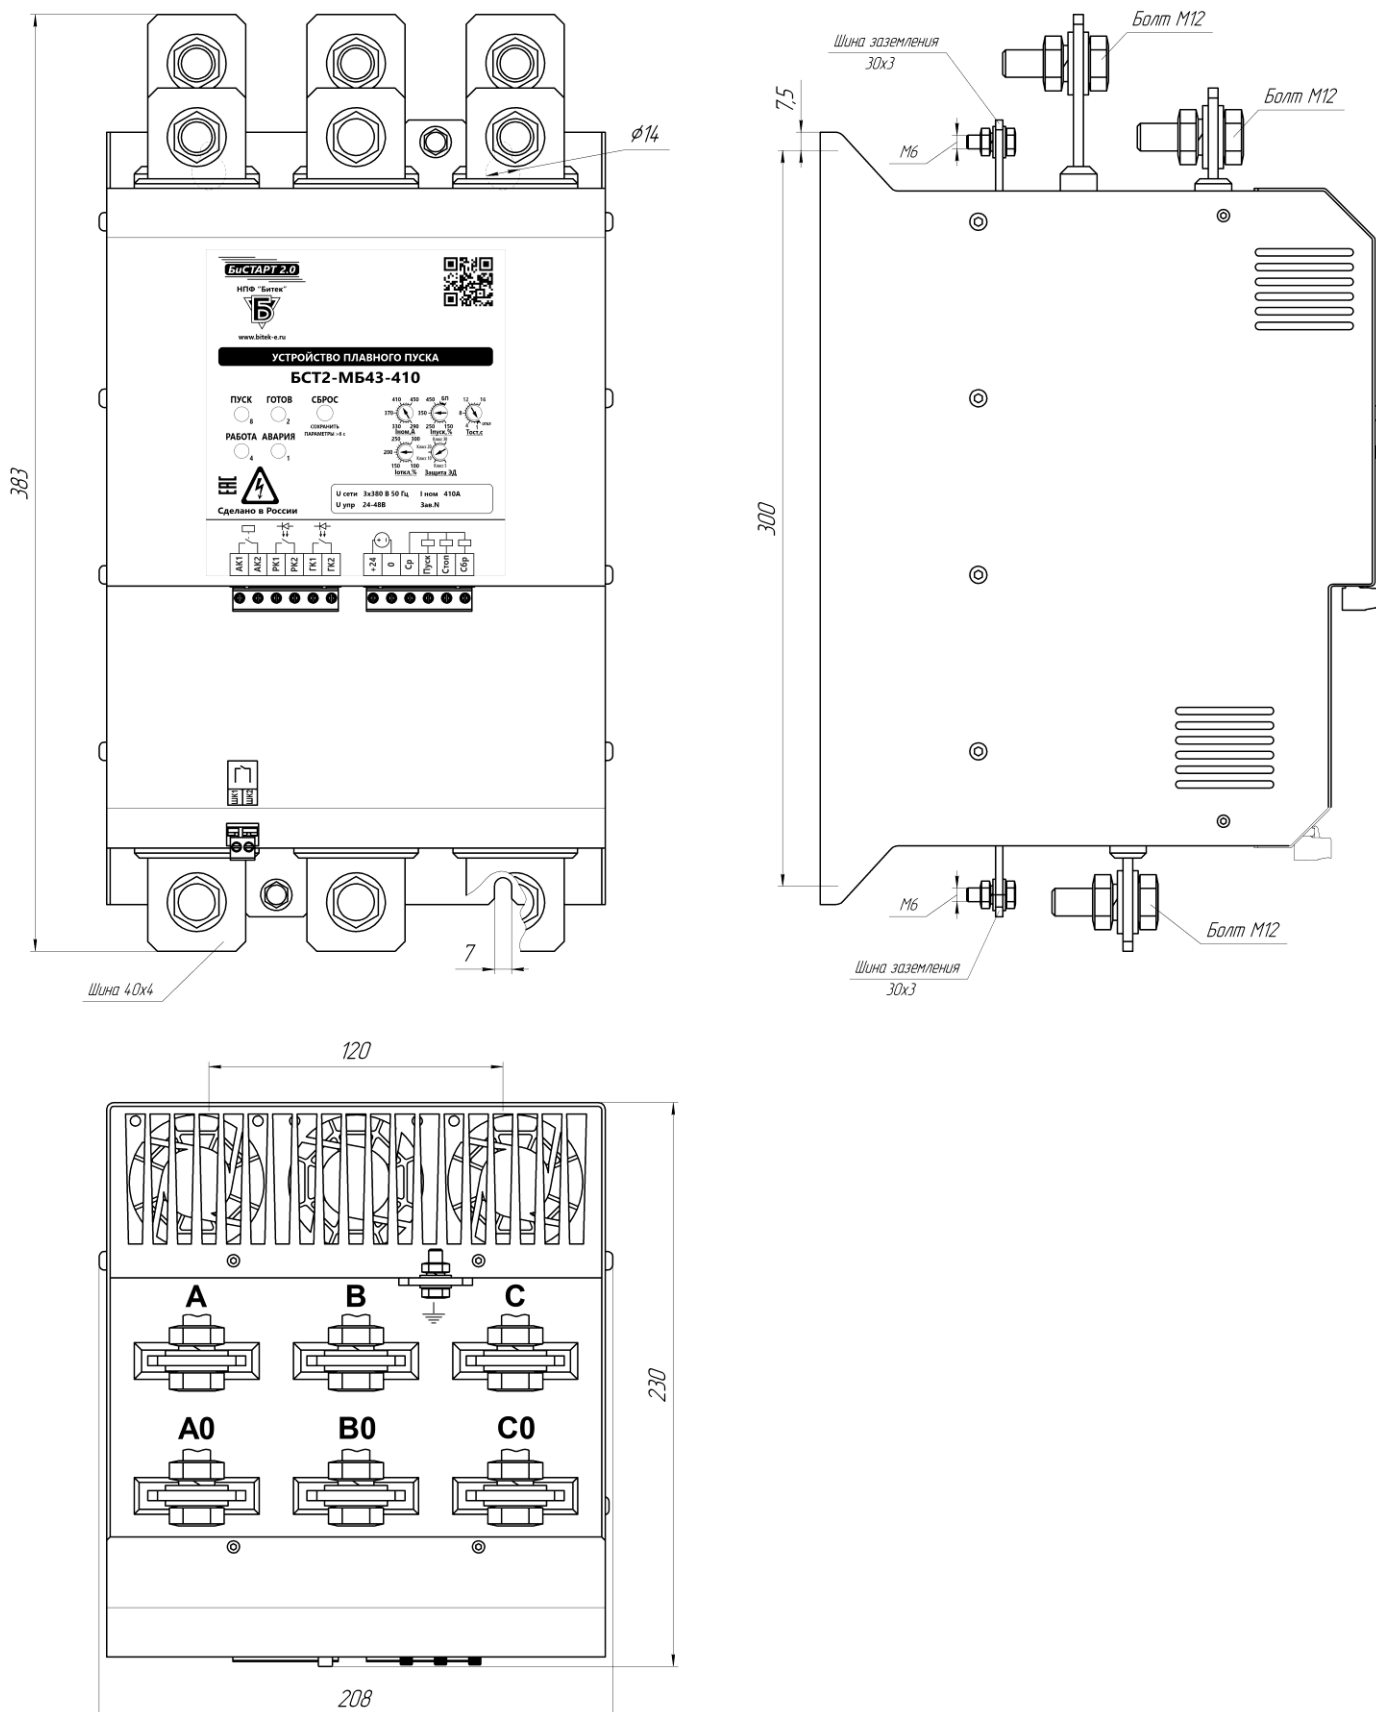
Габаритно-установочные размеры БСТ2-...-250 (-320, -410)
